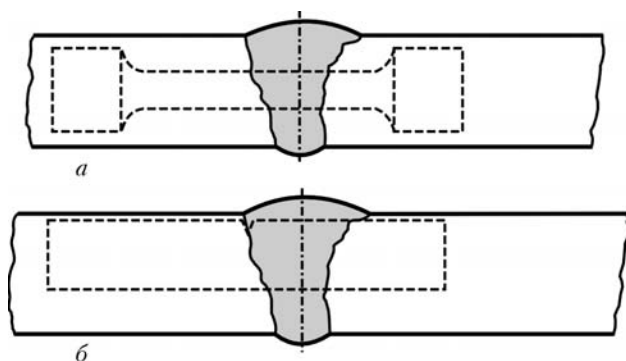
Схема вырезки из темплетов сварных соединений образцов типа II (а) и IX (б) для механических испытаний
